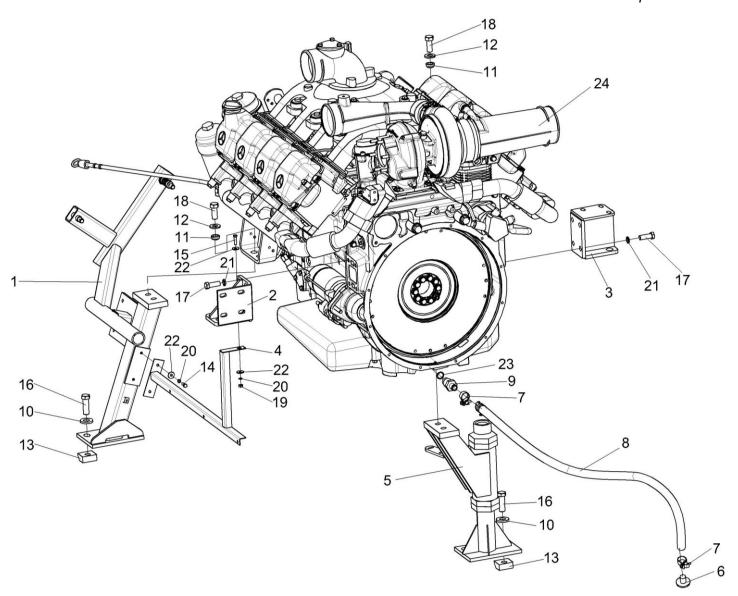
Установка двигателя OM502LA КВК 0150000 (установка двигателя на опорах)
